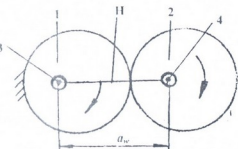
Планетарная передача с эксцентричными круглыми цилиндрическими колесами
